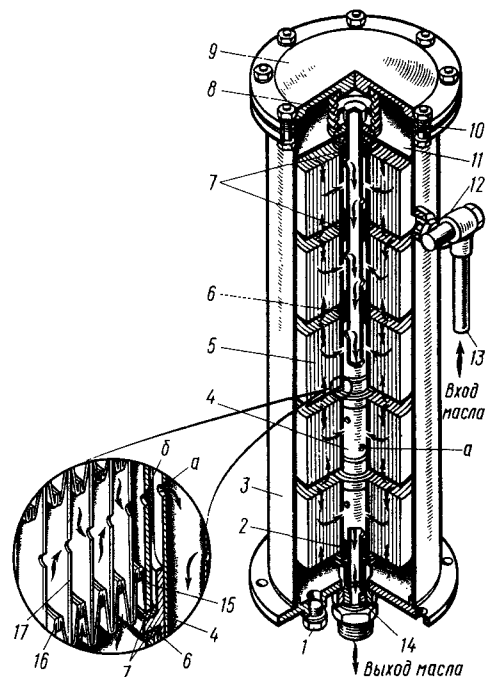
Масляный фильтр тонкой очистки: 1 — сливная пробка; 2 — стальная втулка; 3 — корпус; 4 — стержень; 5 — фильтрующий элемент; 6 — дистанционная втулка; 7 — паронитовая прокладка; 8 — пружина; 9 — крышка; 10 — болт; 11 — центрирующий лист; 12 — перепускной клапан; 13 — маслоподводящая трубка; 14 — штуцер; 15 — пластмассовая втулка; 16 — фильтровальная бумага; 17 — картонная полоса; а, б — радиальные отверстия
